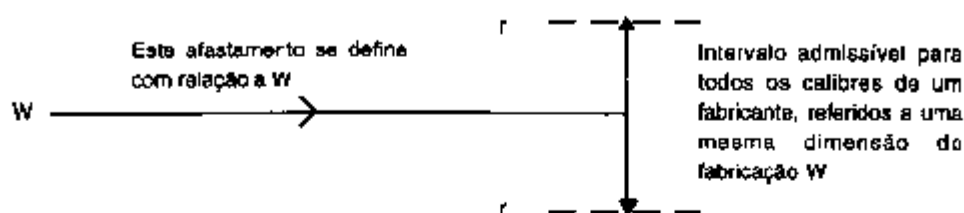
Afastamento de r com relação à dimensão de fabricação W
